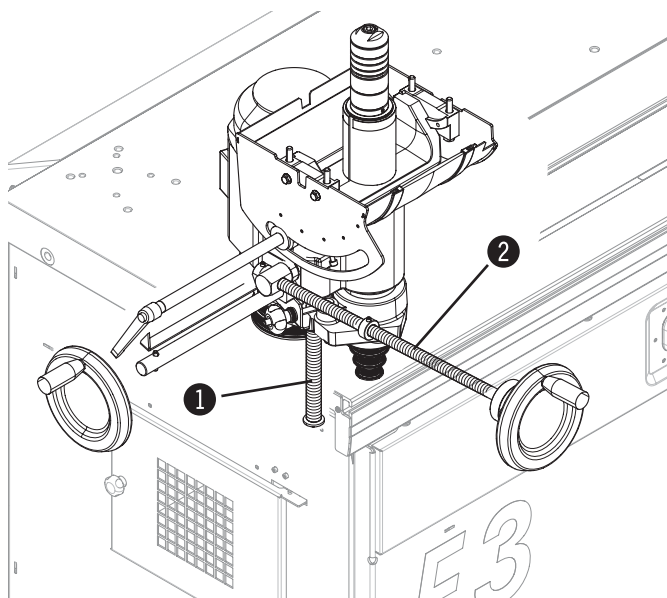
Шпиндель установки высоты/Шпиндель установки угла поворота
